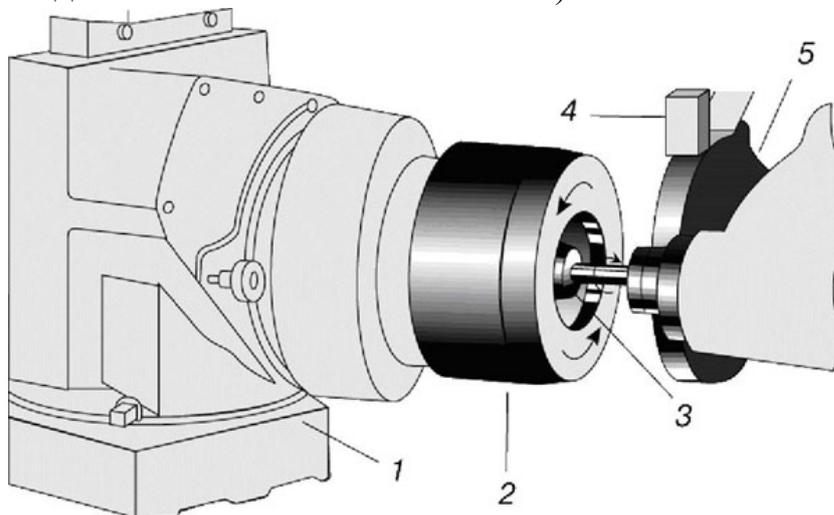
Схема шлифования отверстия в осесимметричной вращающейся заготовке: 1 – делительная бабка; 2 – деталь; 3 – внутренний шлифовальный круг; 4 – отсос пыли; 5 – наружный шлифовальный круг.
